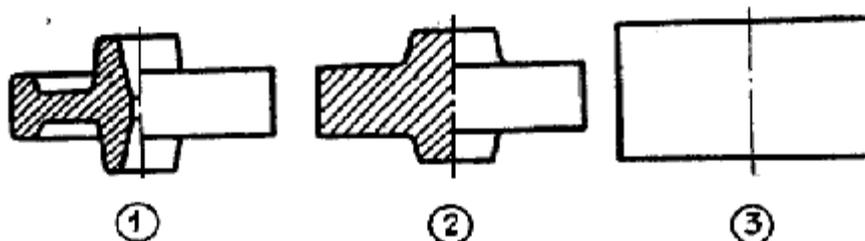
Различные формы заготовок для изготовления зубчатого колеса
